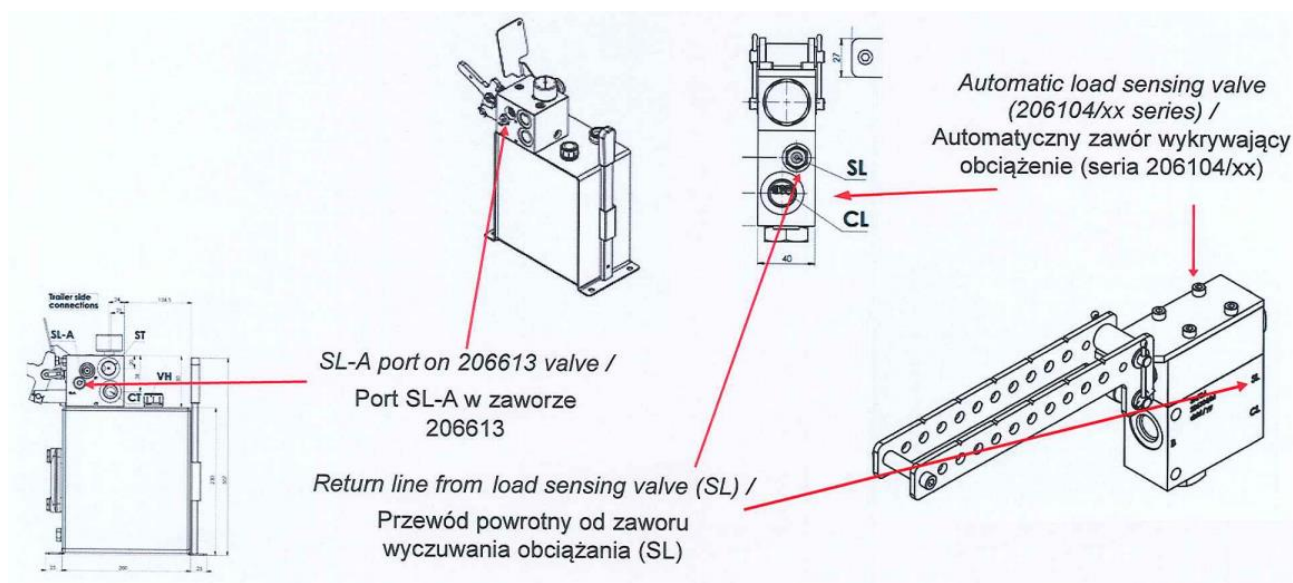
Rzut przedstawiający złącza od strony wału uprawowego.
